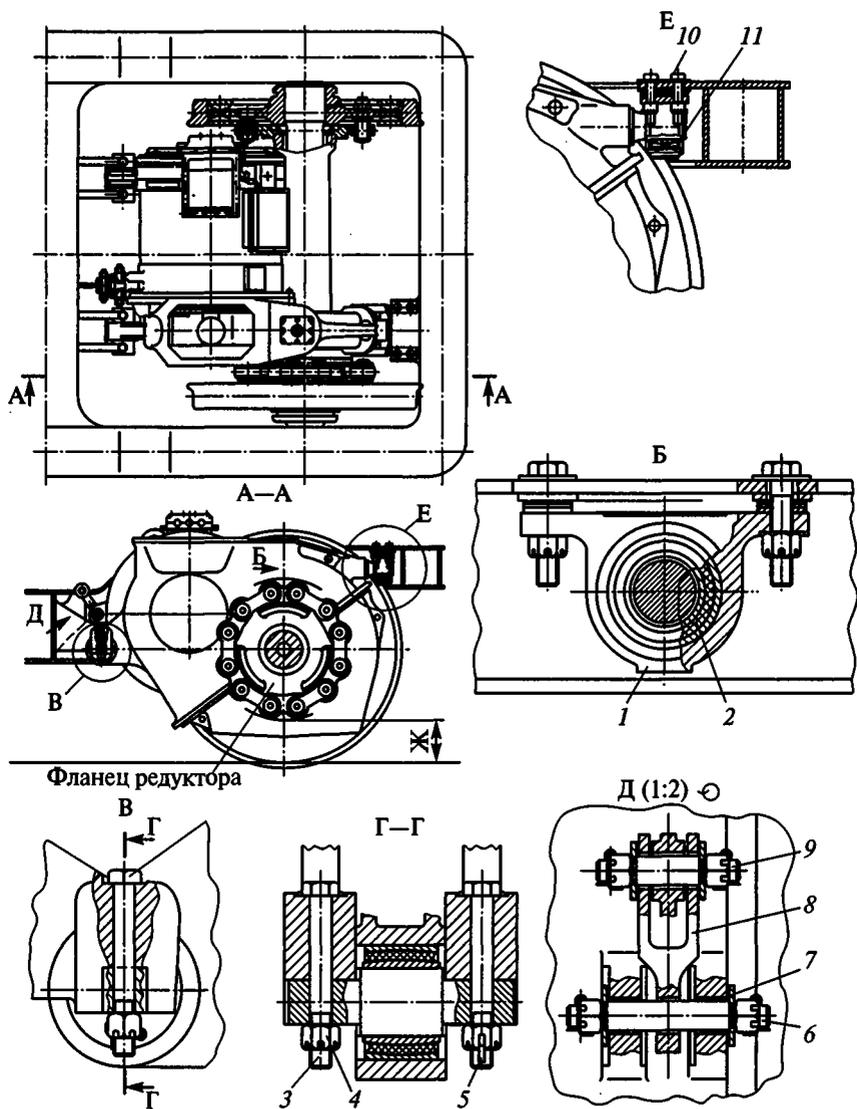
Монтаж колесно-моторного блока на раме тележки:
